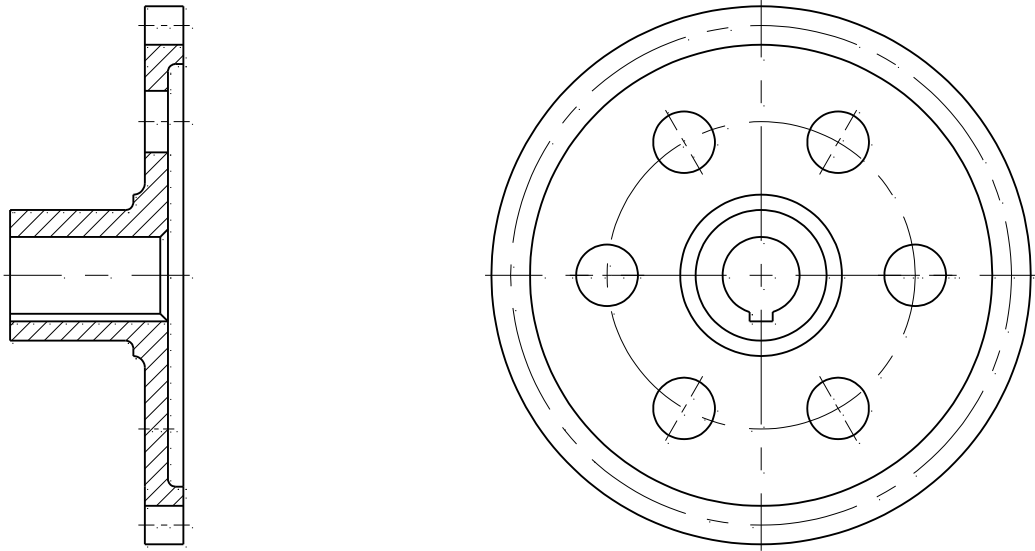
Чертеж зубчатого колеса без размеров
